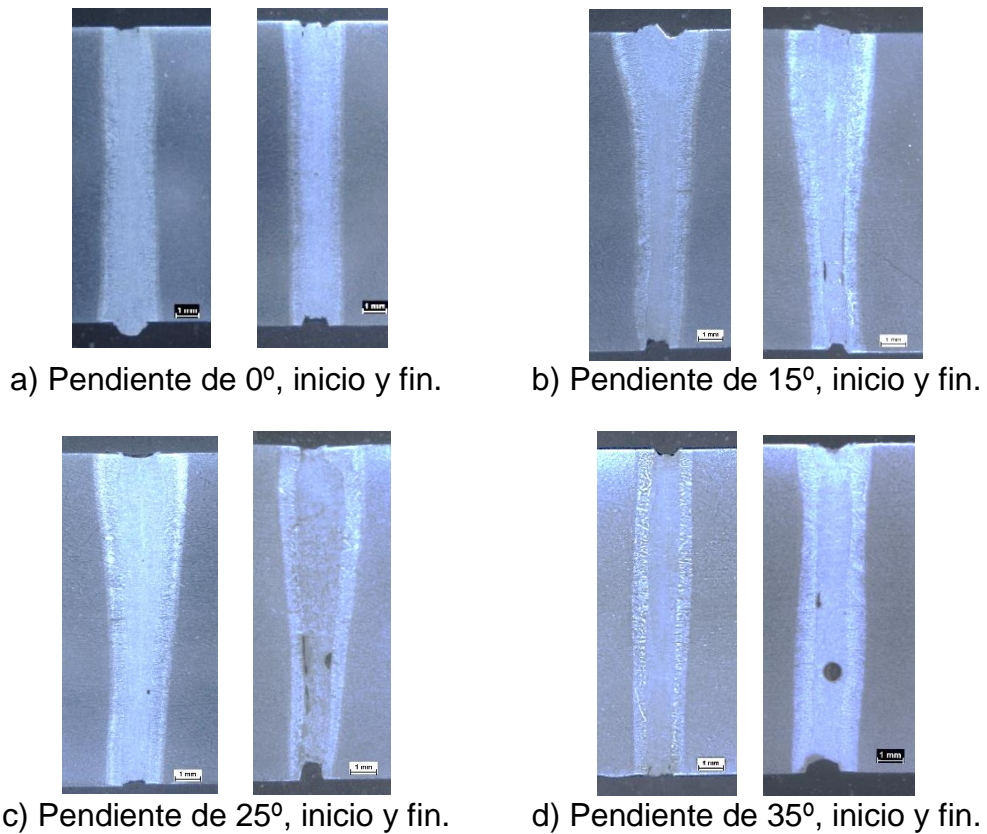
12. Sección transversal de cada cupón soldado por el proceso LBW.
